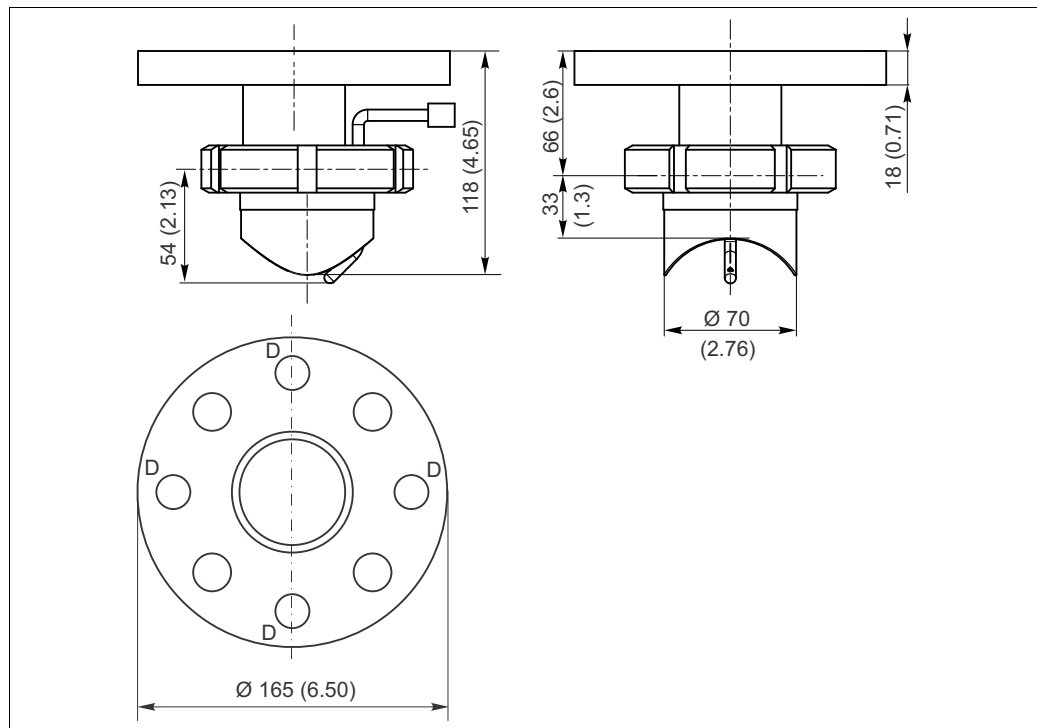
Einschweißspülstutzen, Abmessungen in mm (inch)
